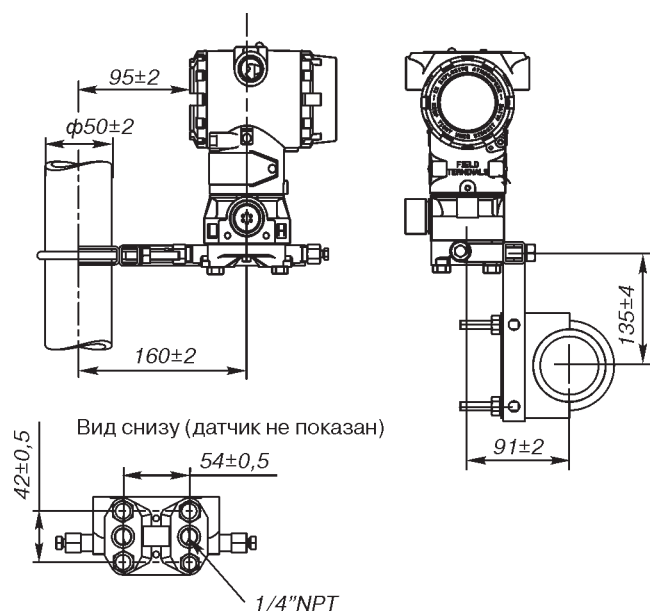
Монтаж на вертикальной или горизонтальной трубе датчиков расходомеров типа MNF, PNF, MFA.
